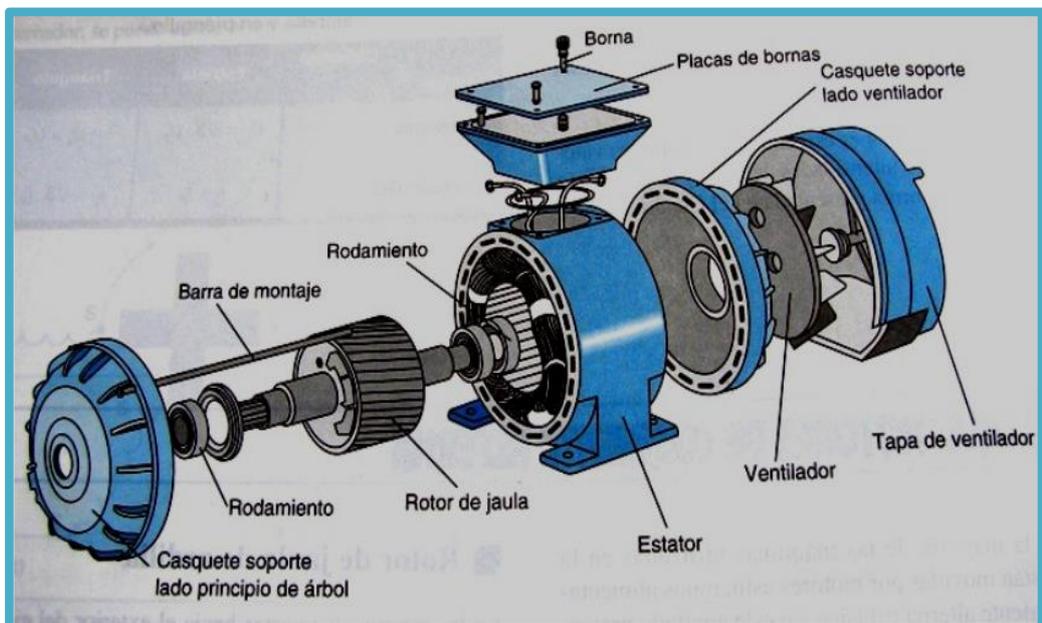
PARTES DEL MOTOR DE ROTOR DE JAULA DE ARDILLA
